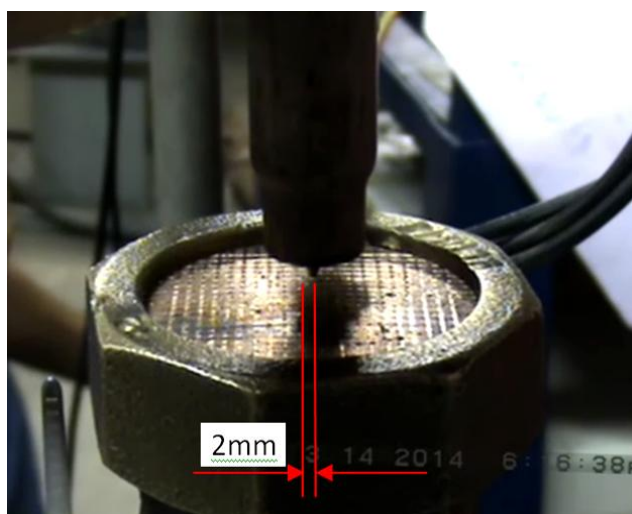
Montagem de um conjunto GTAW para obter arco elétrico estável.
